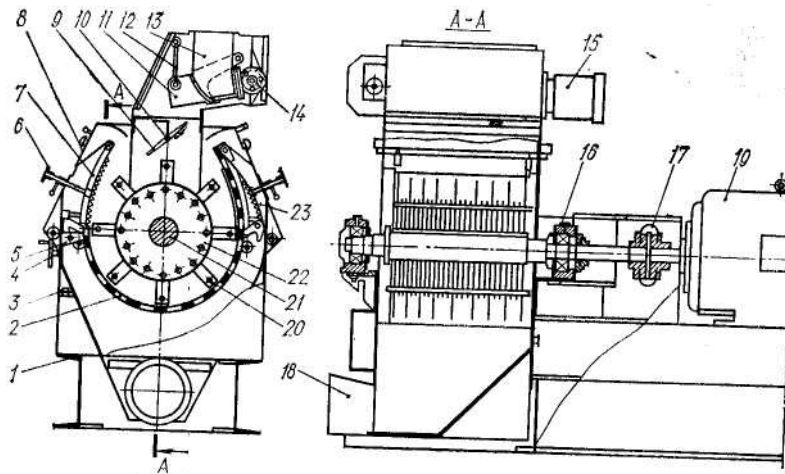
Дробарка молоткова реверсивна А1-ДДР:
